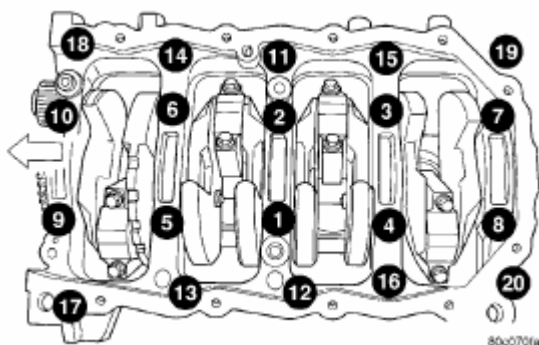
Порядок затяжки болтов крепления крышки коренных подшипников.
